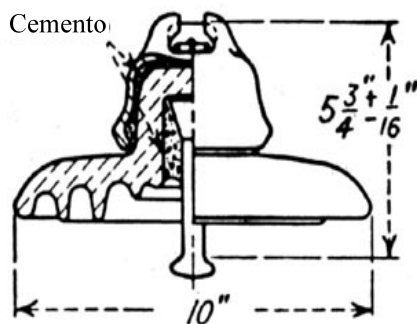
Aislador Ball and Socket Type (Locke Insulator Inc.)
